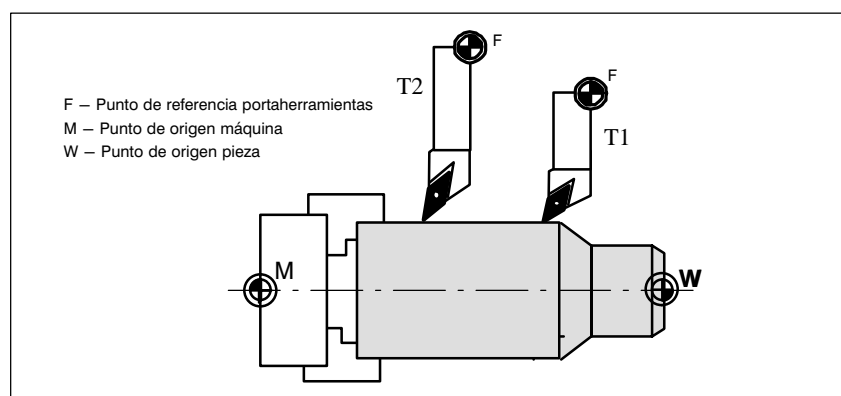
Mecanizado de una pieza con distintas dimensiones de herramienta
